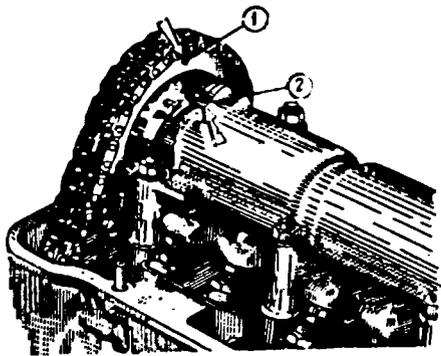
Проверка совпадения установочной метки на звездочке распределительного вала с меткой на корпусе подшипников: 1 - метка на звездочке; 2 - метка на корпусе подшипников
